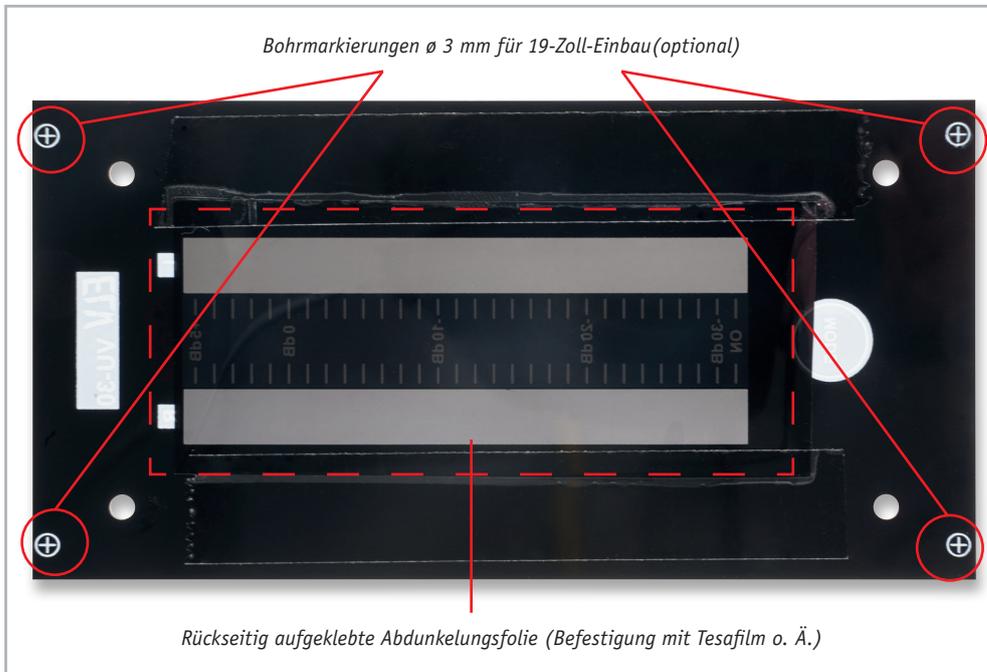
Die Rückseite der Frontplatte mit aufgeklebter Abdunkelungsfolie (optional). Hier sind auch die Bohrmarkierungen für die mögliche Montage in einem 19-Zoll-Rack zu sehen.
